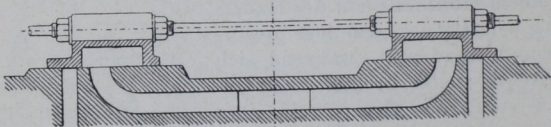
Stellung des Schiebers im Niederdruckzylinder.
